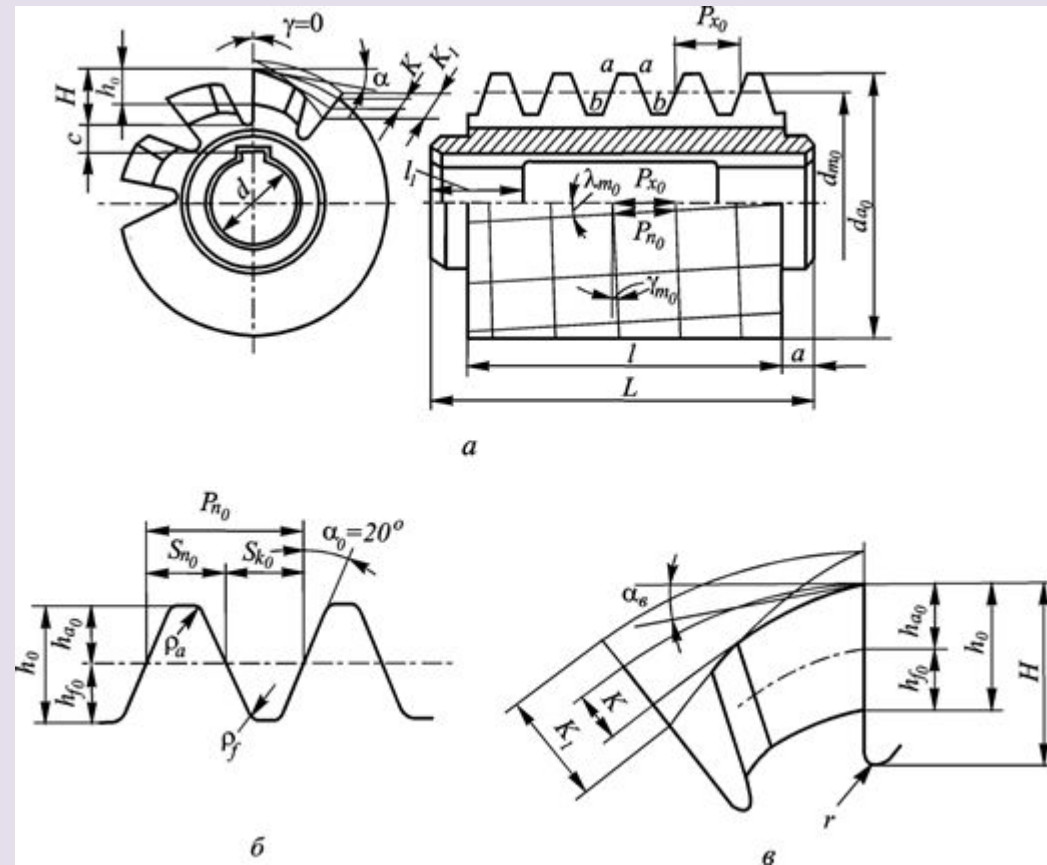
Червячная модульная фреза: а – конструктивные элементы и геометрические параметры; б – профиль зуба в нормальном сечении; в – параметры зуба червячной фрезы
